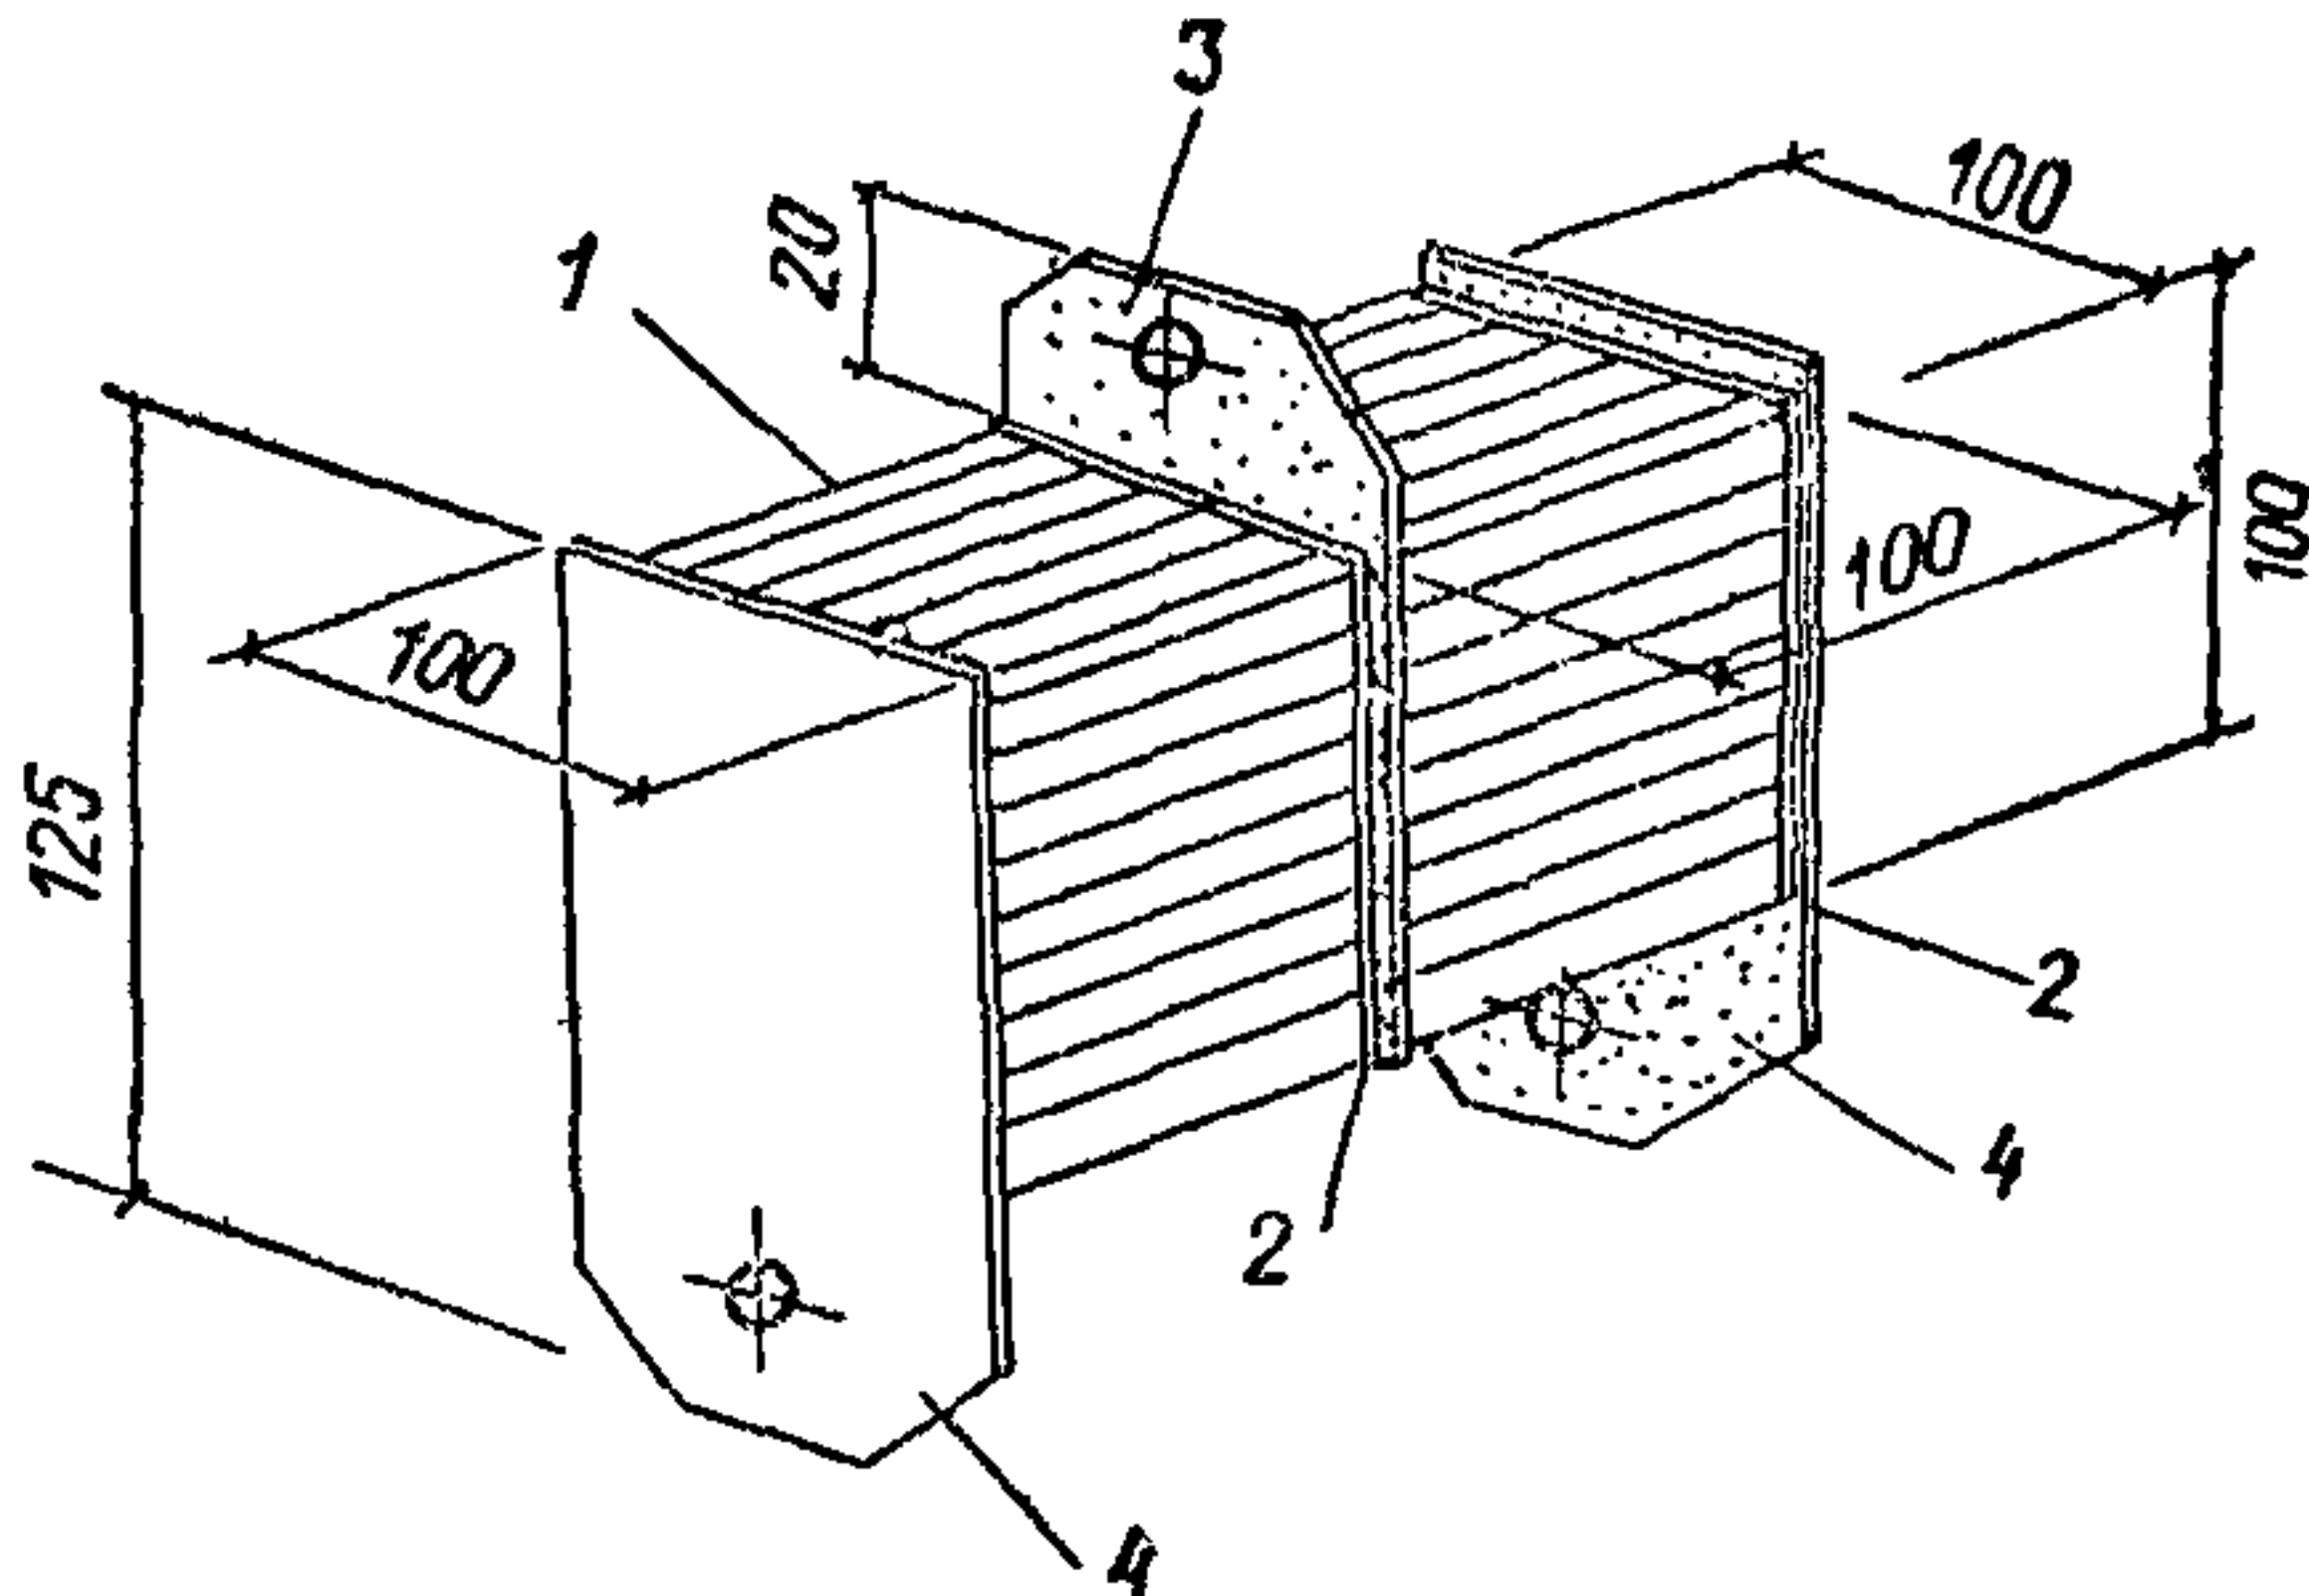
Форма и размеры спаренного составного образца для испытания прочности при сдвиге сотопласта
